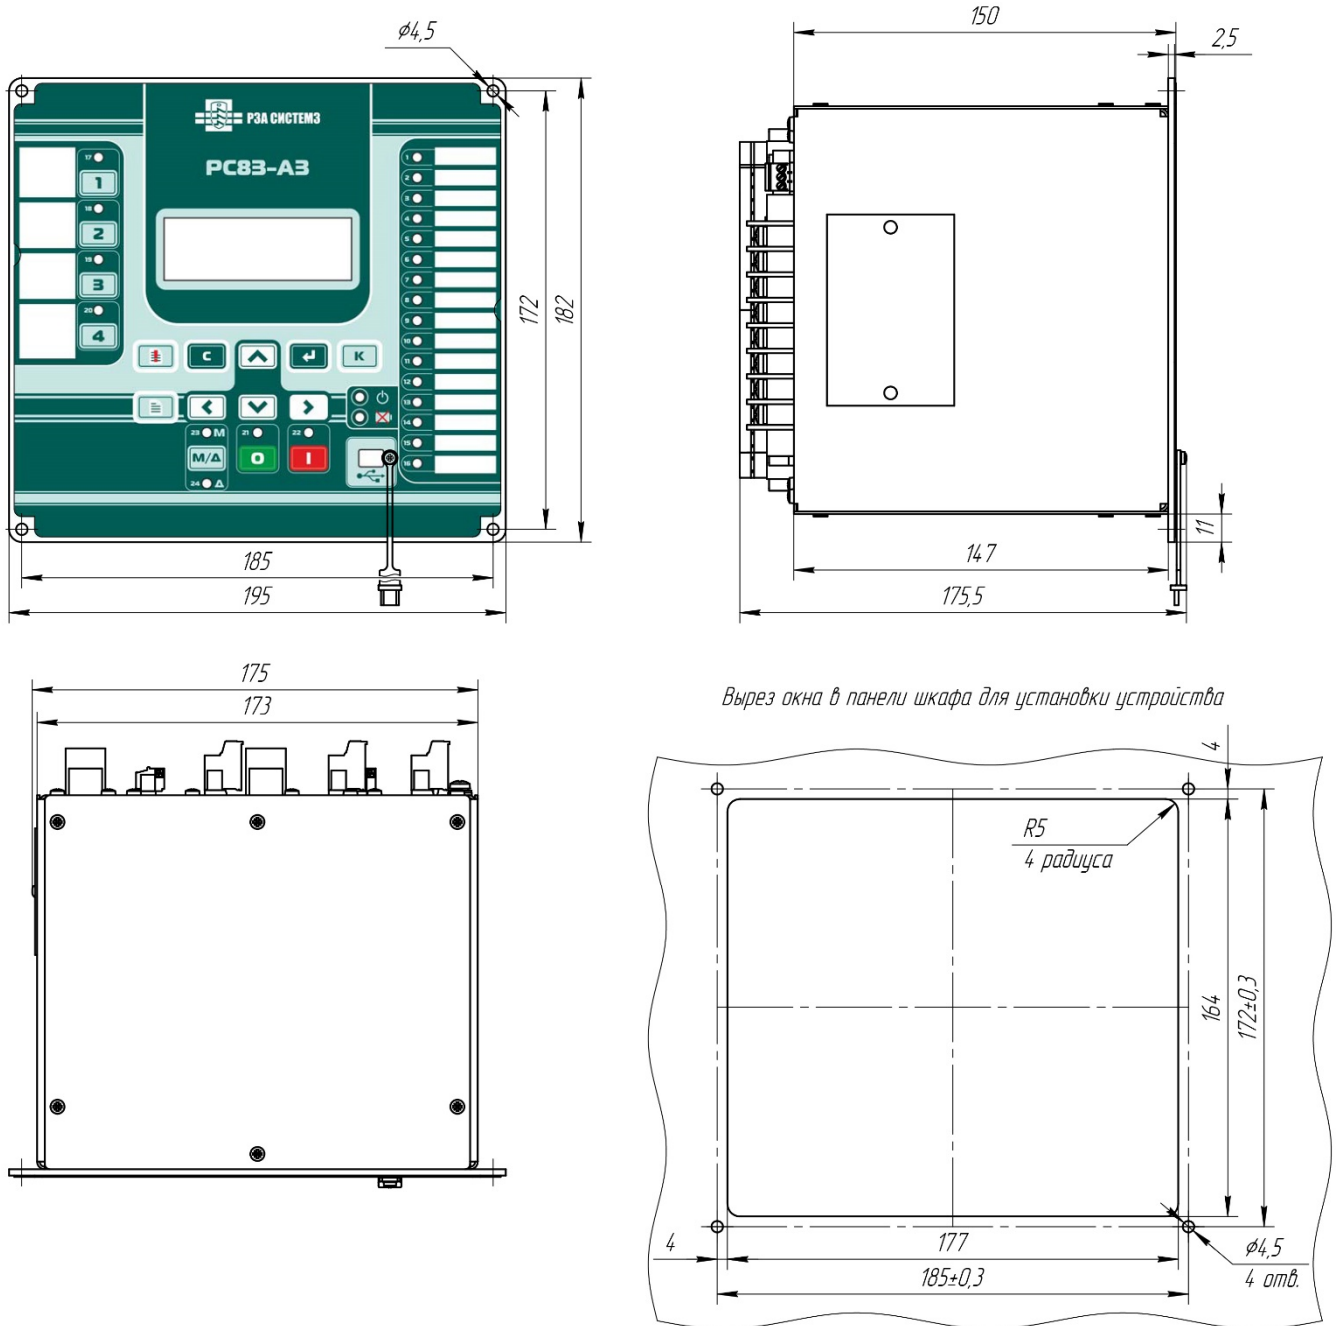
Габаритные и присоединительные размеры устройства РС83-А3
